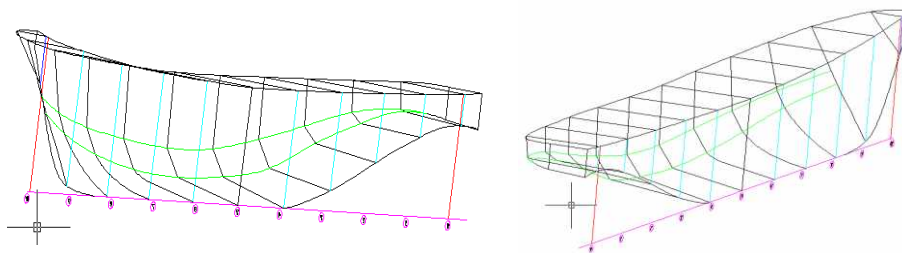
3D-модель наружной обшивки в AutoCAD
